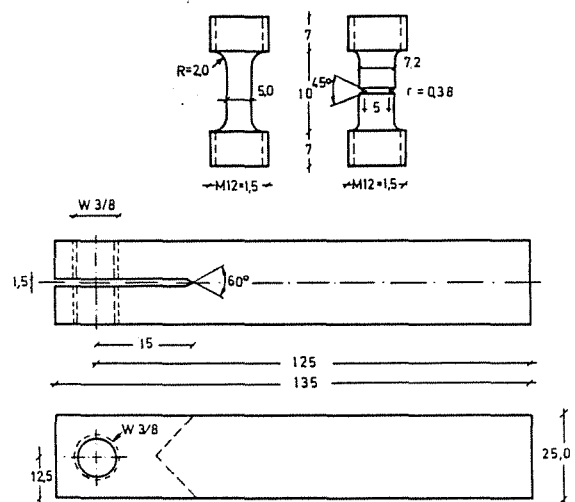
Tipos y dimensiones, en mm., de las probetas.
